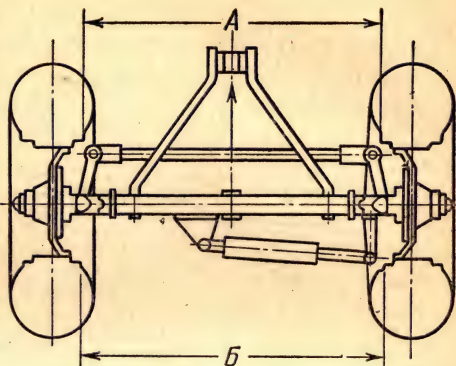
Схема проверки схождения управляемых колес (колеса показаны в плане, стрелка указывает направление рабочего движения колес).
